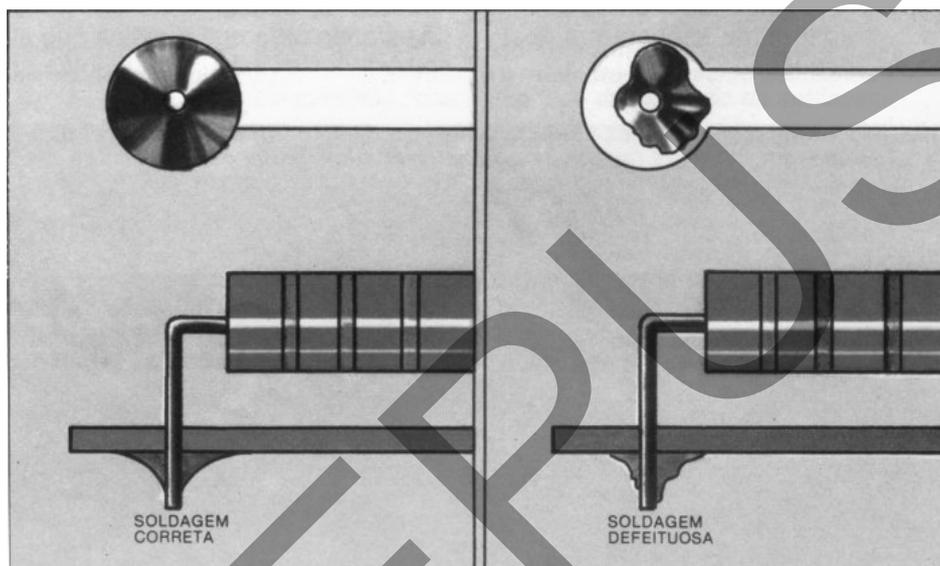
Exemplos de soldagem correta e defeituosa (extraído de [1]).
